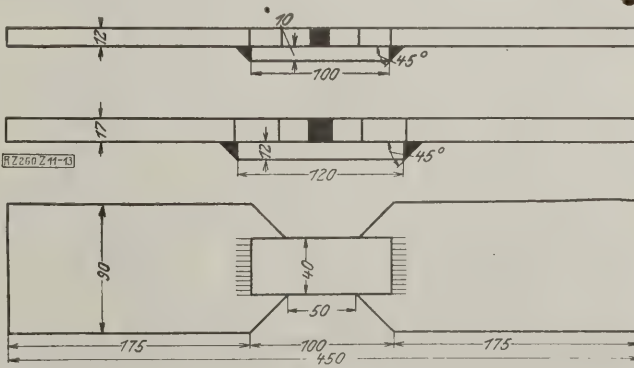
bis 13. Probestäbe mit einseitig angeschweißter Lasche.
